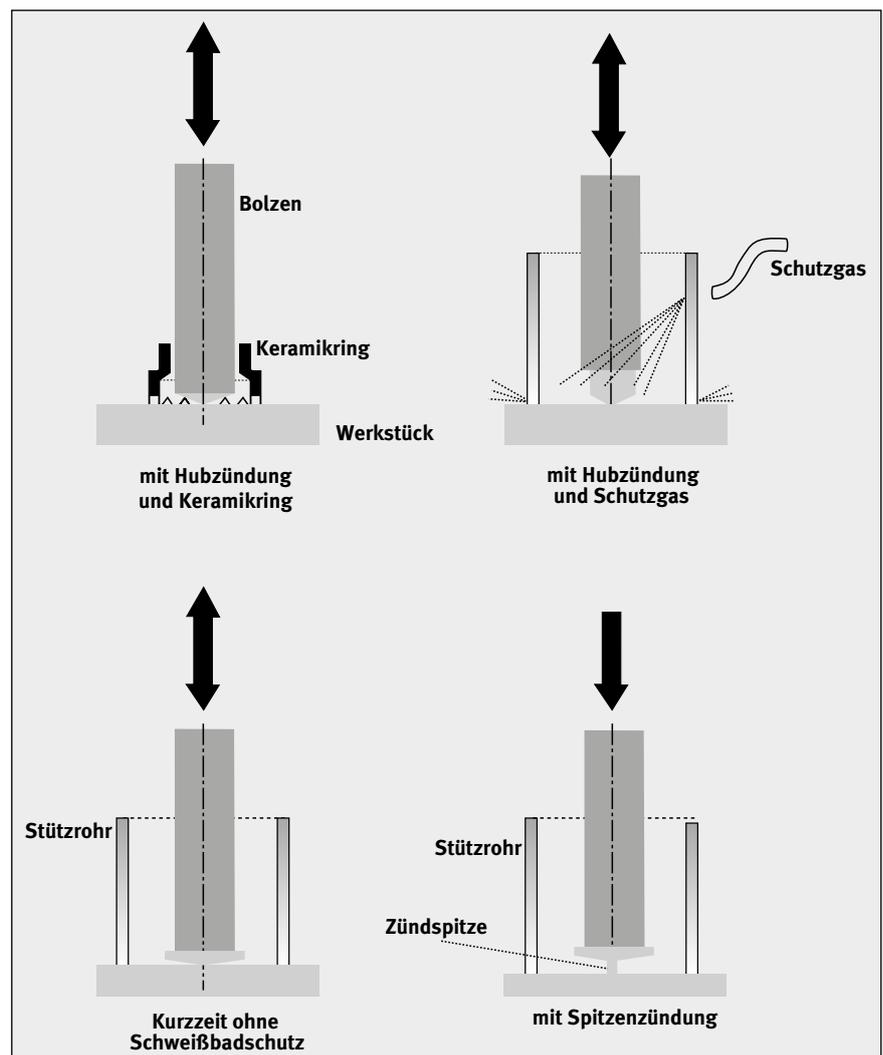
Die wichtigsten Verfahrensvarianten beim Lichtbogenbolzenschweißen
